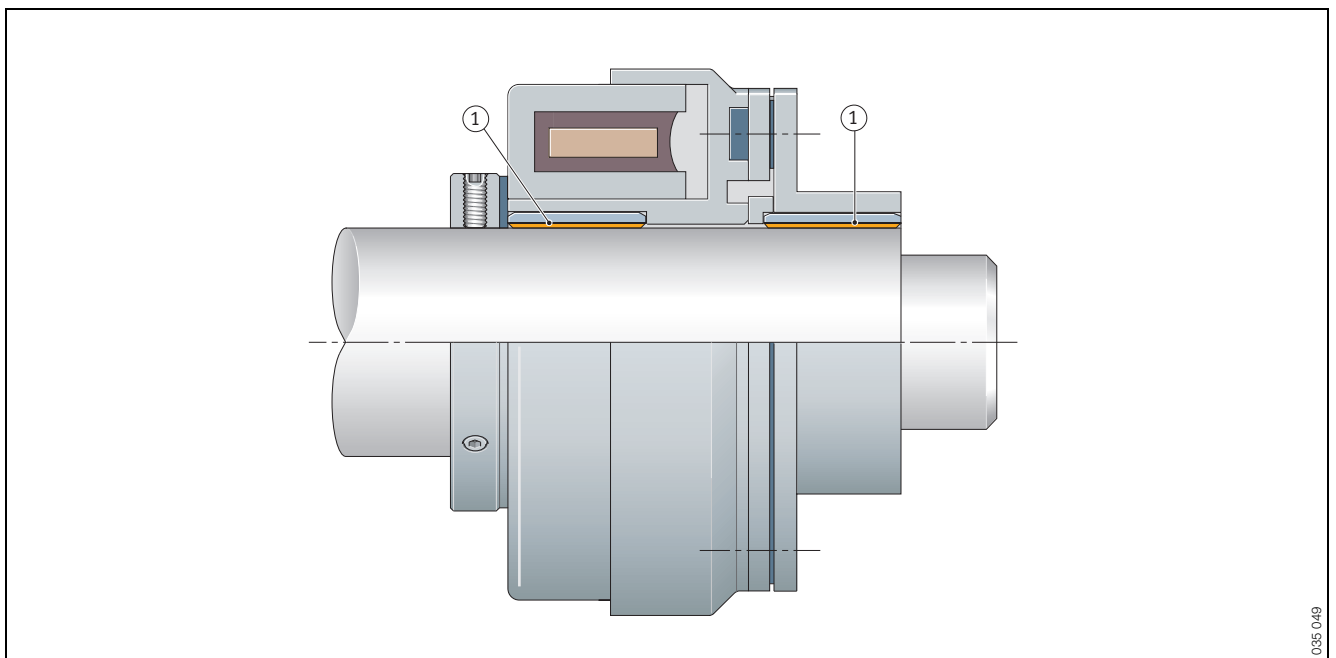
· Elektromagnet mit Buchsen ① aus P141 unter linearer Bewegung
